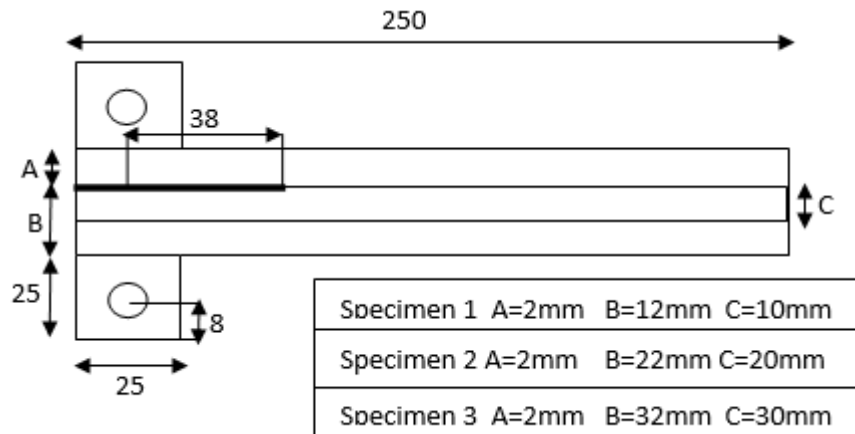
Eprouvette d'une poutre DCB (Double Cantilever Beam) [6].
